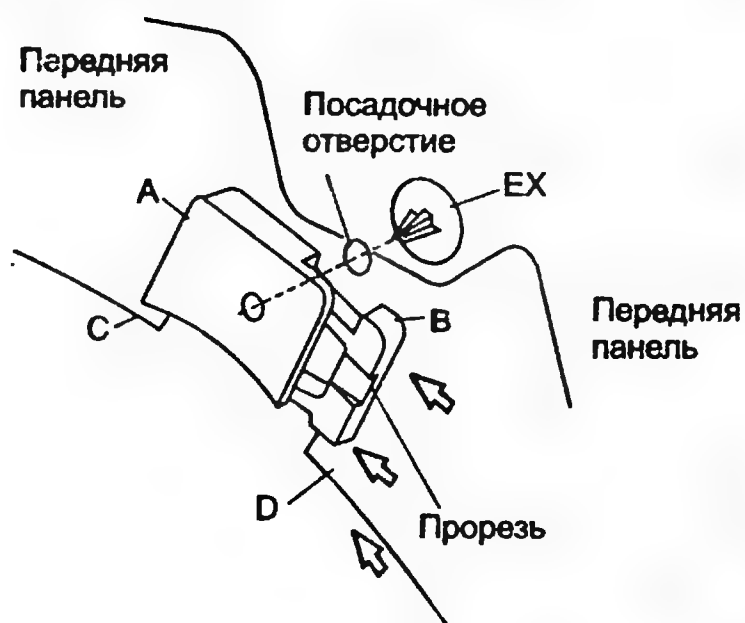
Демонтаж уплотнителя дверцы люка
